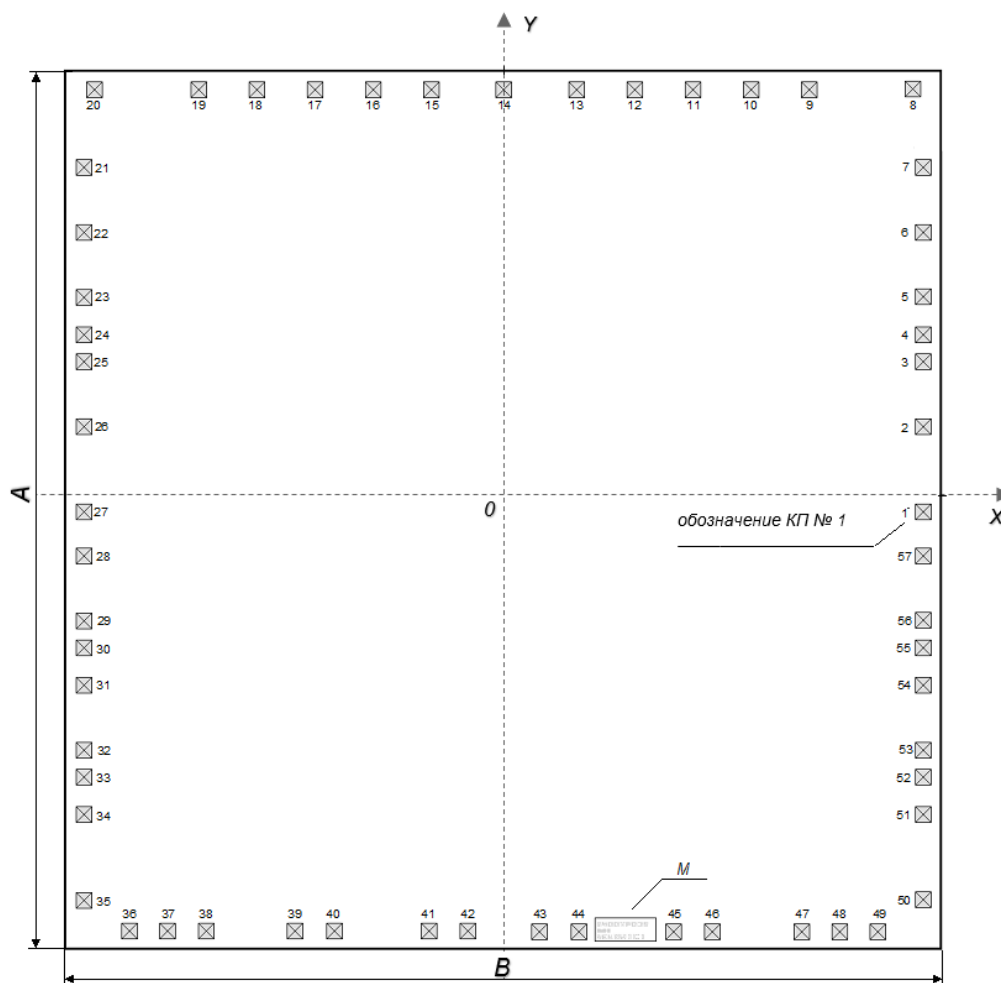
Габаритный чертеж кристалла 5400TP03H4
